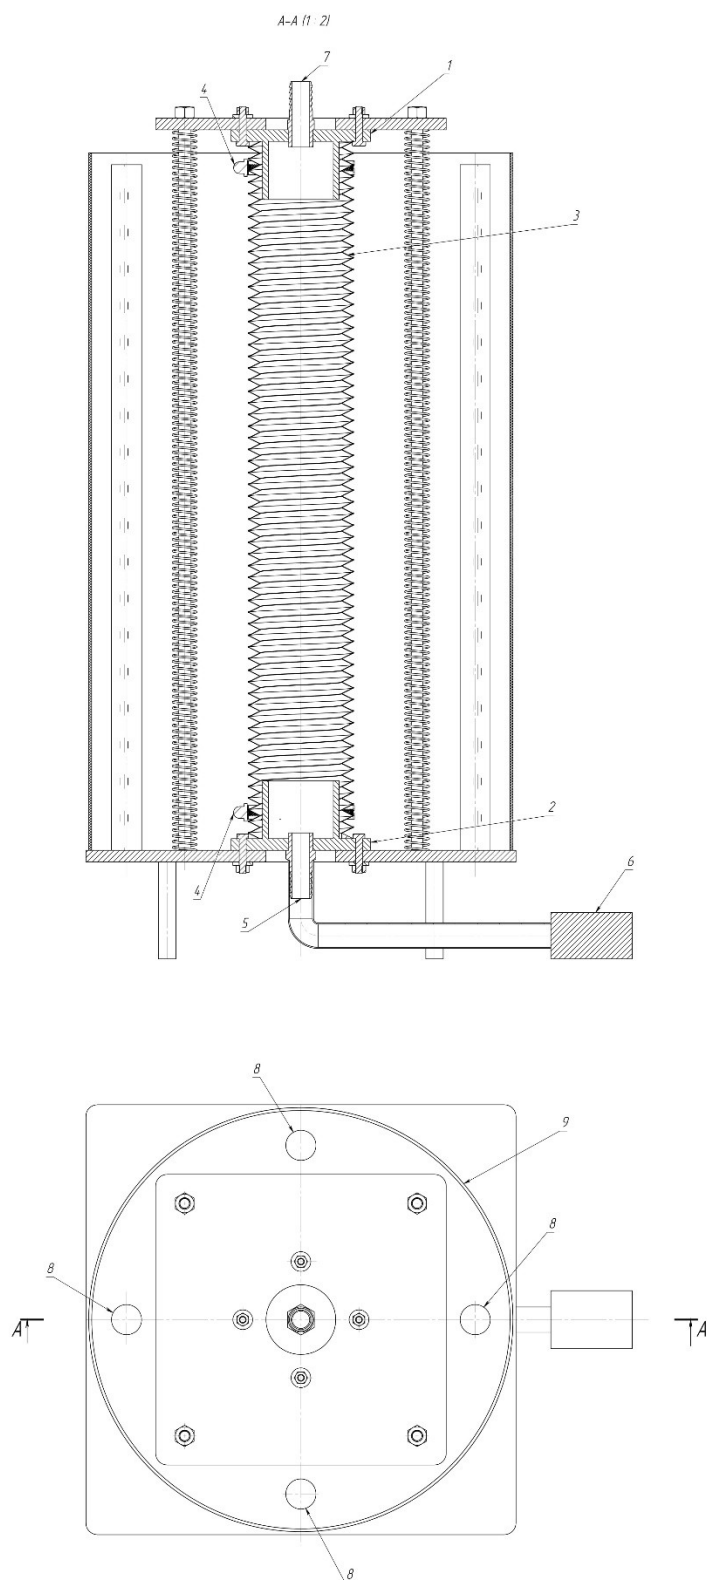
Схема лабораторного фотобіореактора
